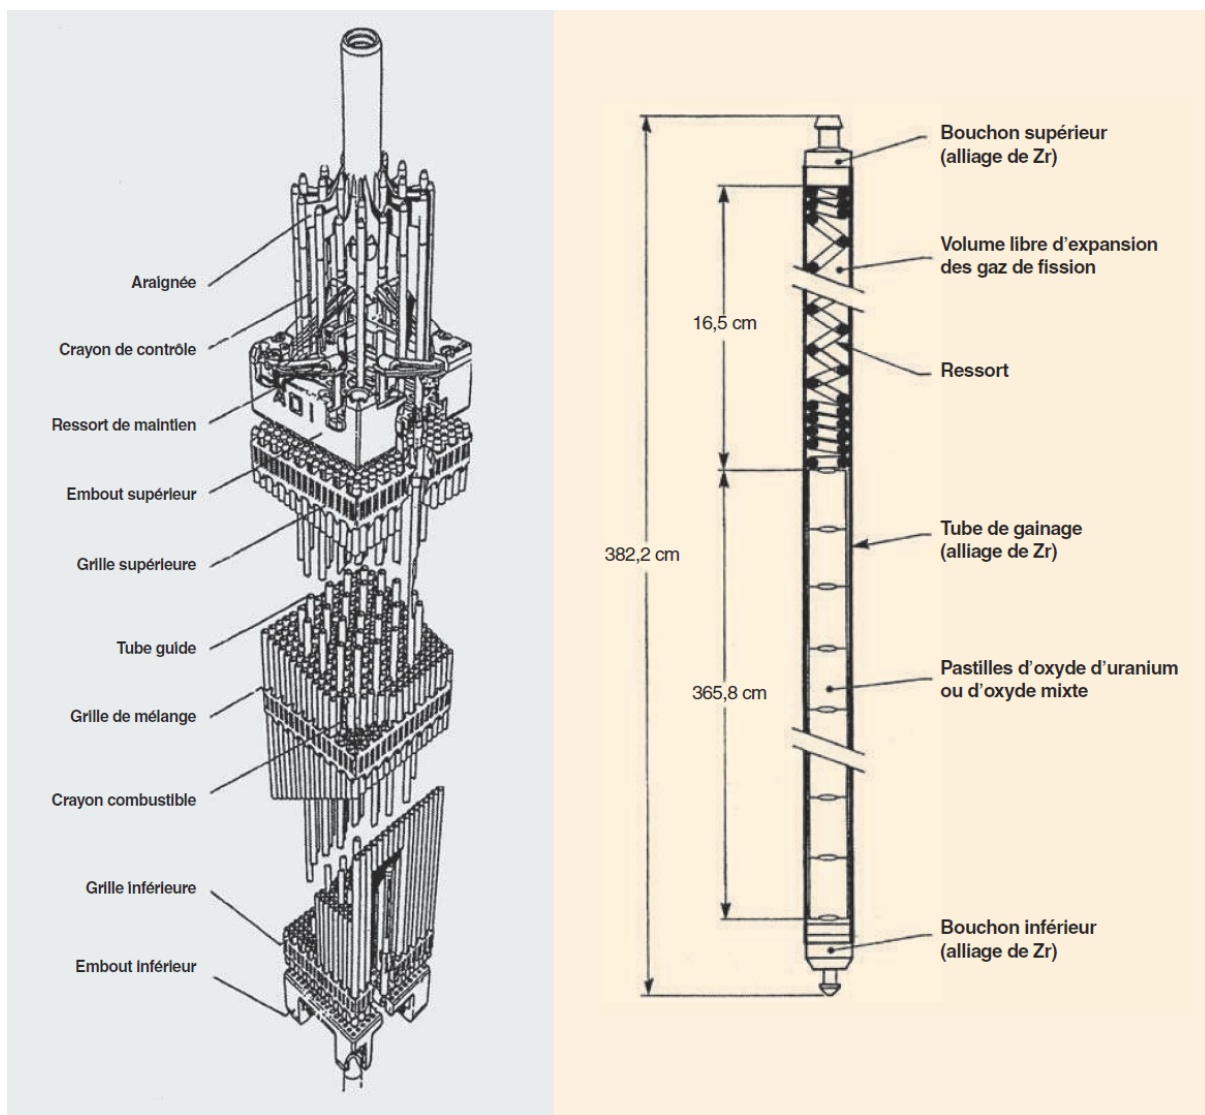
Crayon et assemblage combustible UOX [14]
